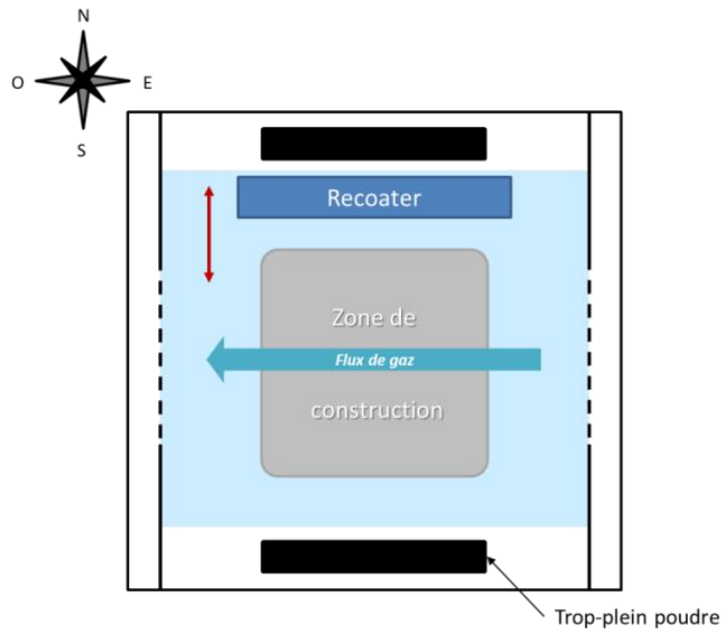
POSITIONNEMENT DU PATEAU DE CONSTRUCTION DANS LA CHAMBRE DE CONSTRUCTION
